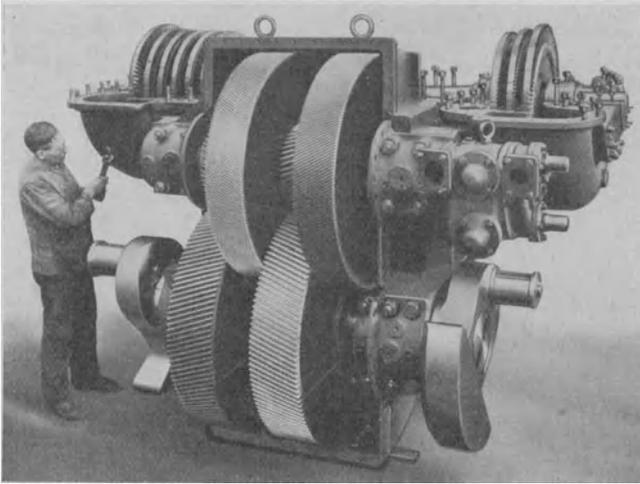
Zahnradvorgelege für die Kruppsche Turbinenlokomotive.
